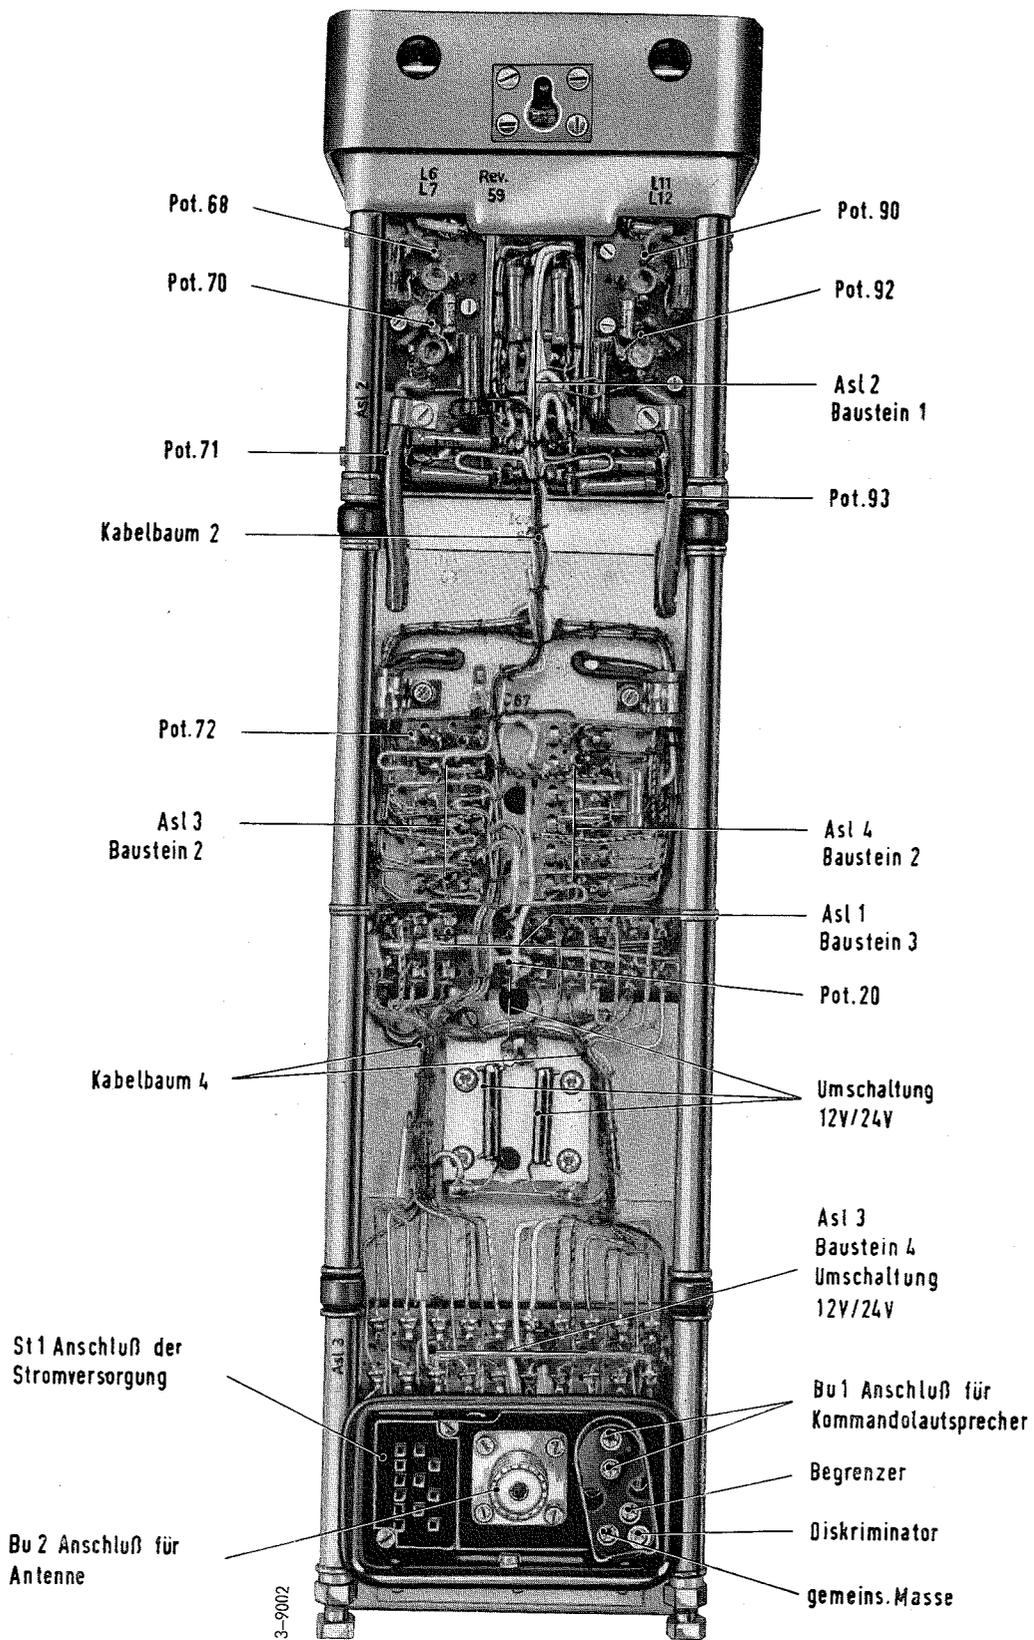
SE-Gerät FuG 7a geöffnet, Ansicht der Buchsenseite
